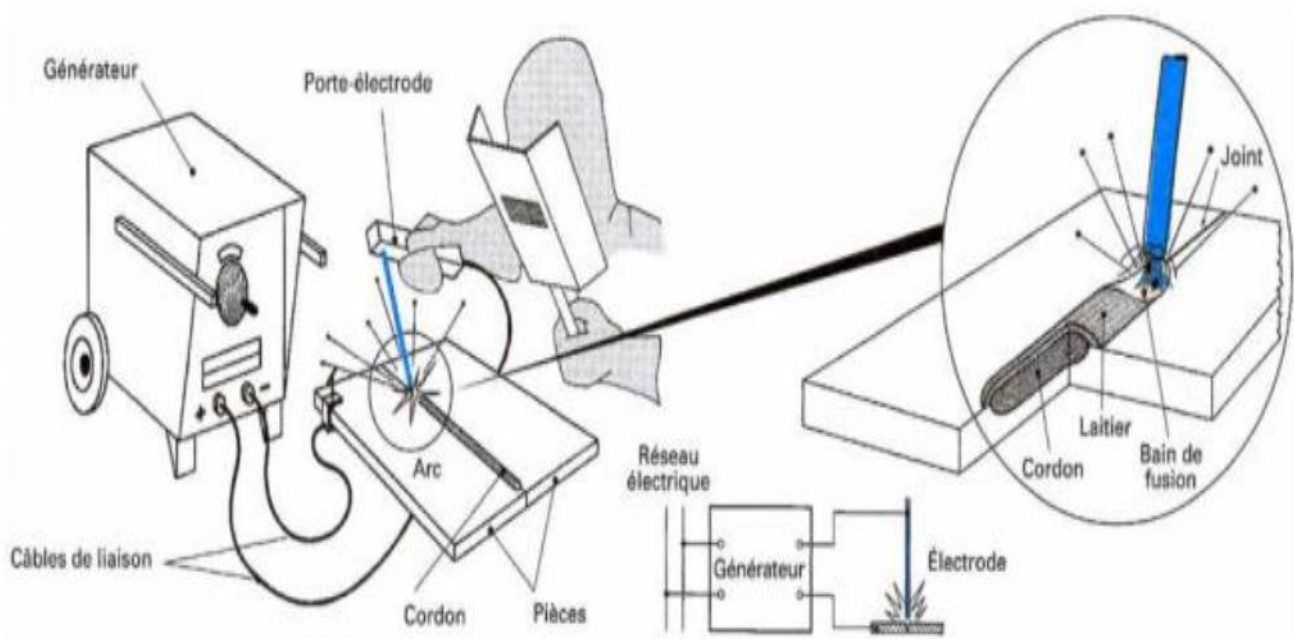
Soudage à l'arc avec électrode enrobé [11].
